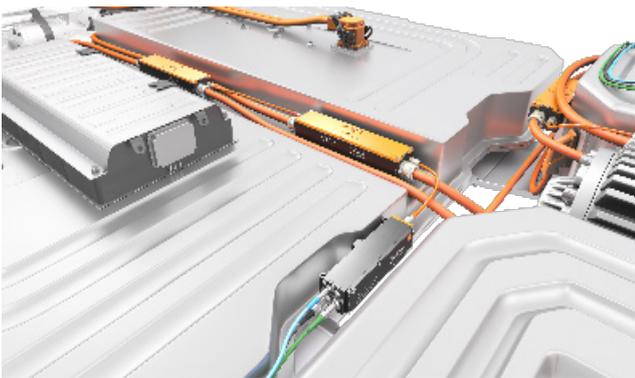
und Abb. 3: Flexibler Einbau der Messtechnikkomponenten
